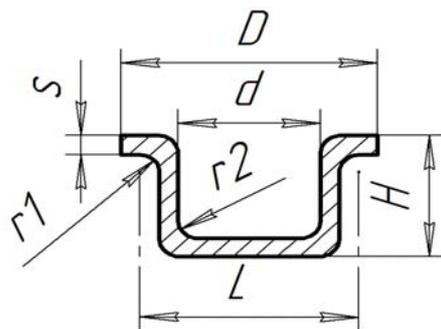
Деталь с фланцем, получаемая вытяжкой
